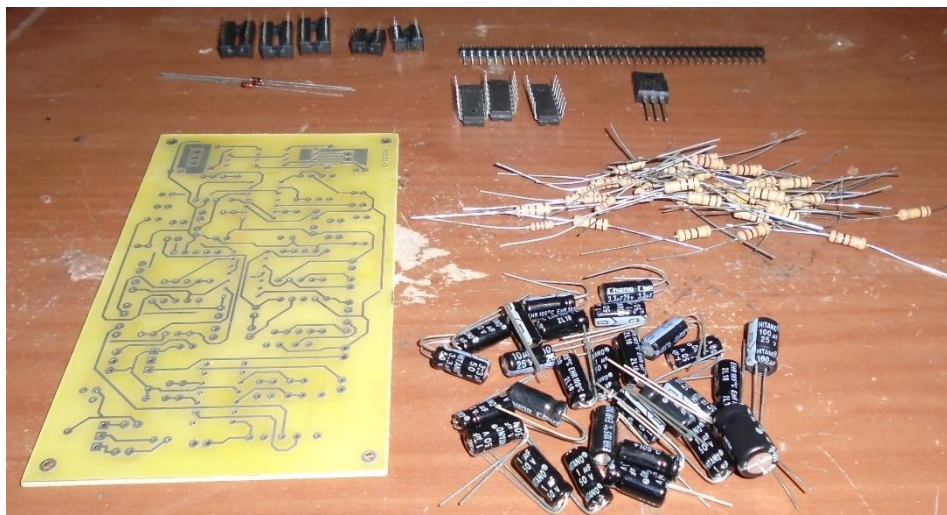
PCB del circuito de acondicionamiento y elementos a soldar
